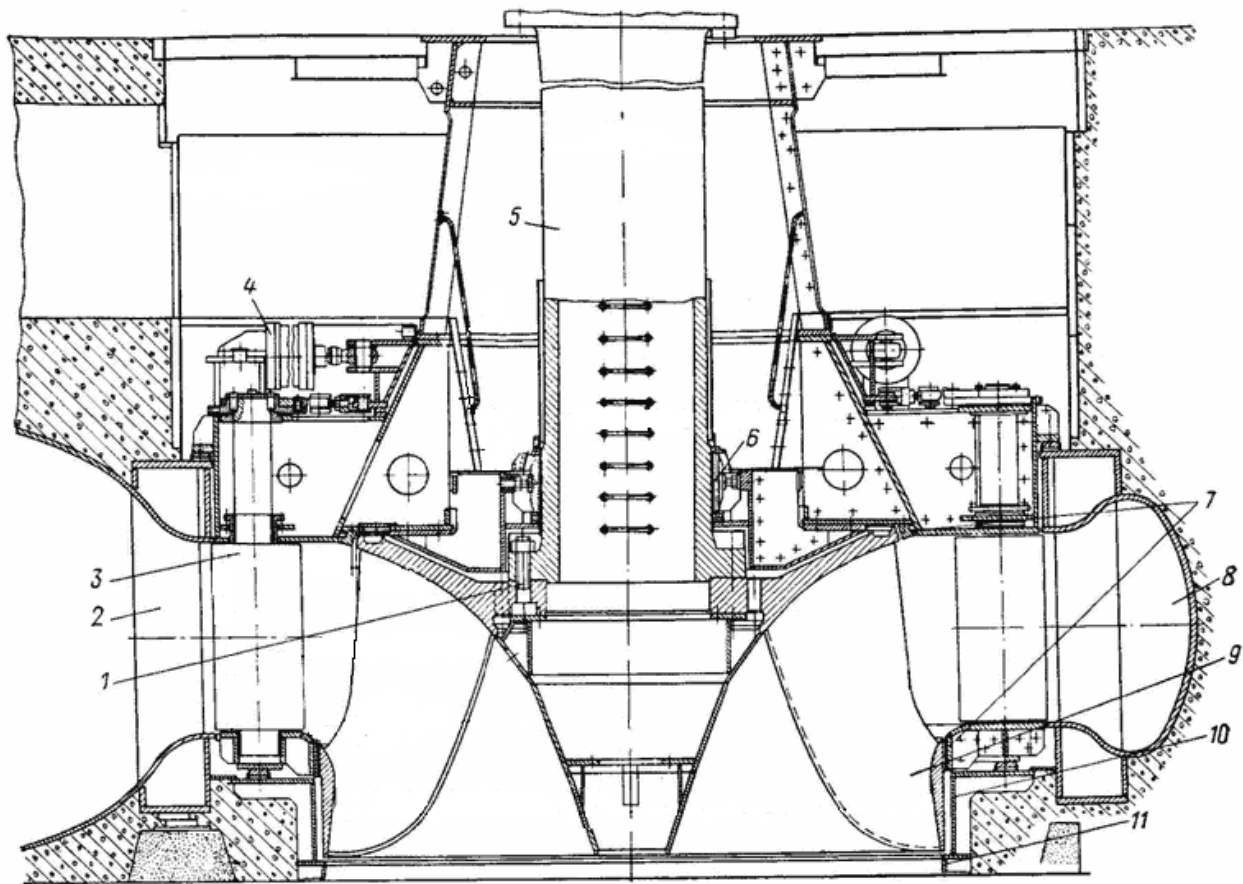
Разрез радиально-осевой гидротурбины: 1 – приспособанный болт; 2 – статор; 3 – сопловой аппарат; 4 – масляной сервомотор; 5 – вал; 6 – направляющий подшипник; 7 – кольца; 8 – металлическая сварная камера; 9 – рабочее колесо.
